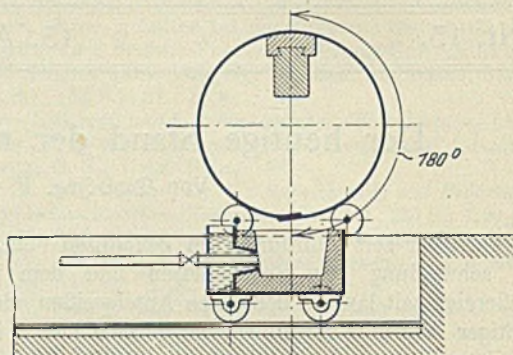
Kesselschweißung mit Koksfeuer.
